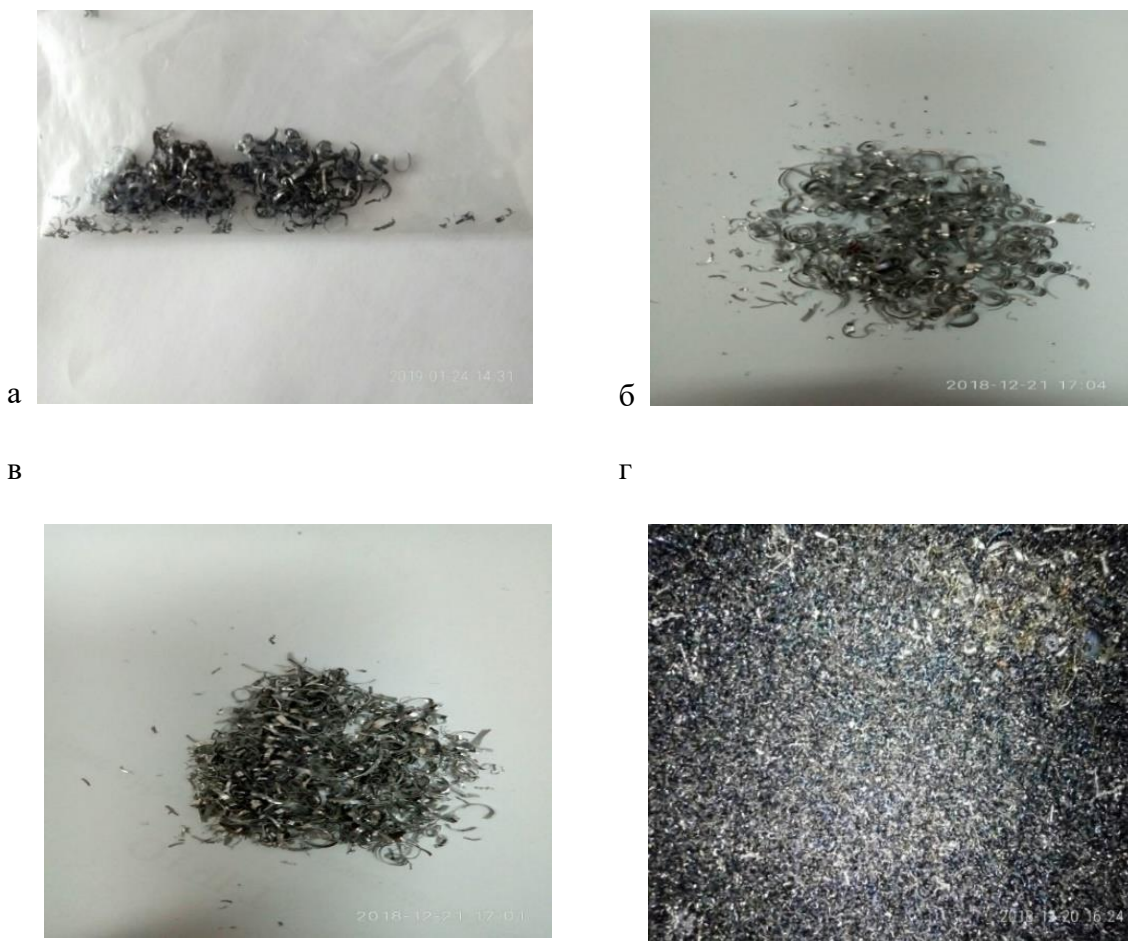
Фотографии типов стружки: а – из титанового сплава марки ВТ22; б - стружки из алюминиевого сплава марки АК 4; в - стружки из алюминиевого сплава марки В 95; г – стружки из стали марки 45Х
